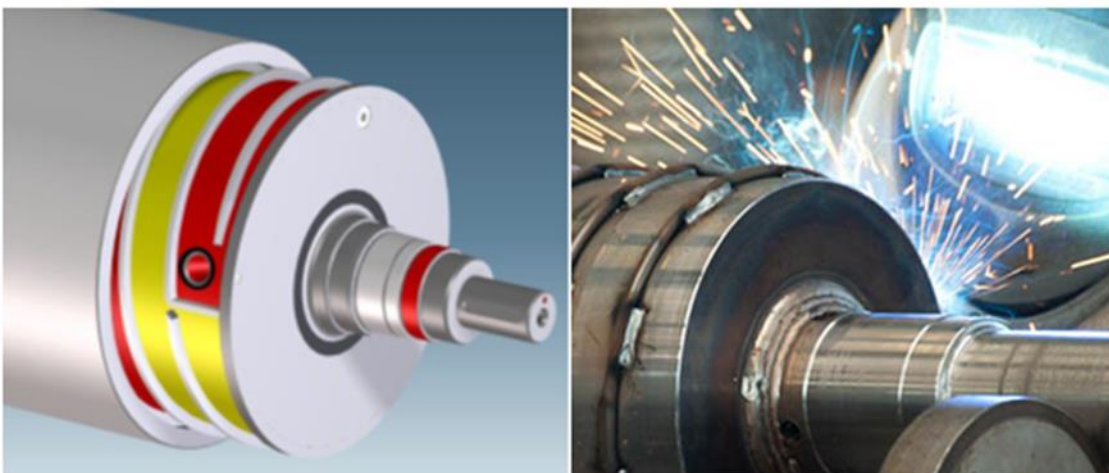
Innenkörper mit Spiralen, gedreht oder geschweißt
